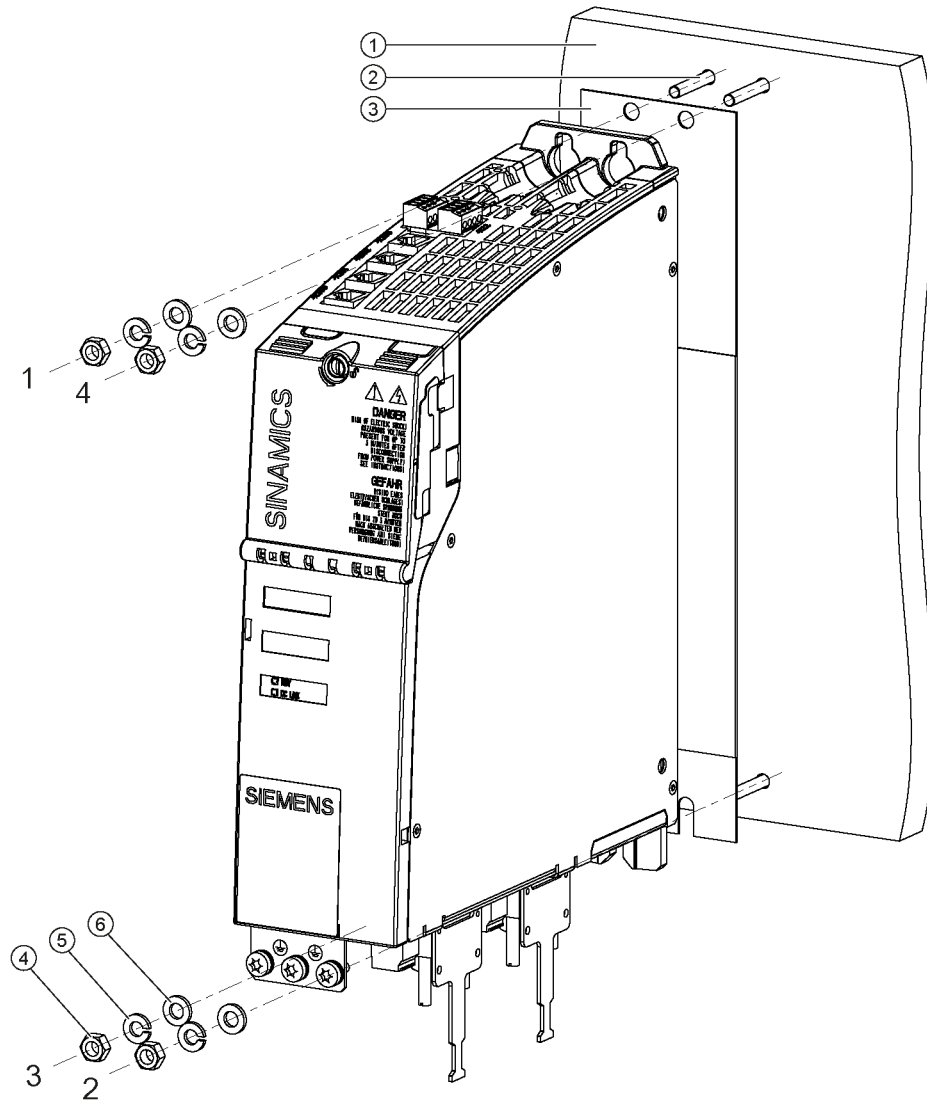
Montaje de Motor Module Booksize Compact con refrigeración por aire interna
